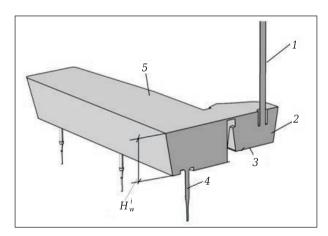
Модель жидкого металла для анализа процесса разливки стали открытой струей из СРК в пятиручьевой ПК сортовой МНЛЗ: 1 — струя металла из СРК; 2 — плоскость симметрии пятиручьевого ПК сортовой МНЛЗ; 3 — металл в приемной камере ПК; 4 — металл, поступающий из разливочных стаканов ПК в кристаллизаторы; 5 — зеркало металла в ПК; $H_{\rm w}^{\rm i}$ — рабочий уровень металла в ПК
